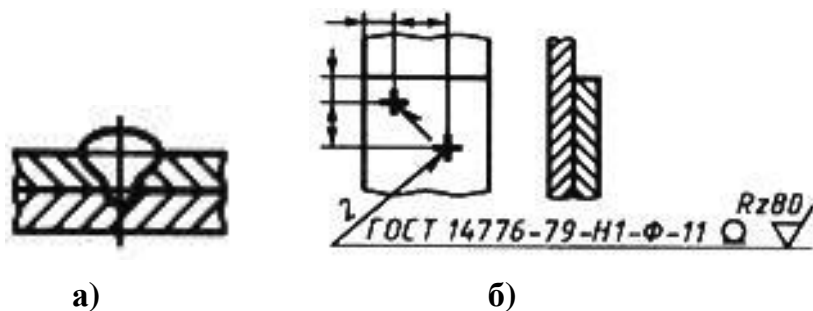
Пример обозначения сварного шва [5]: а – форма поперечного сечения шва; б – обозначение с лицевой стороны (обозначение с оборотной стороны не предусмотрено)
